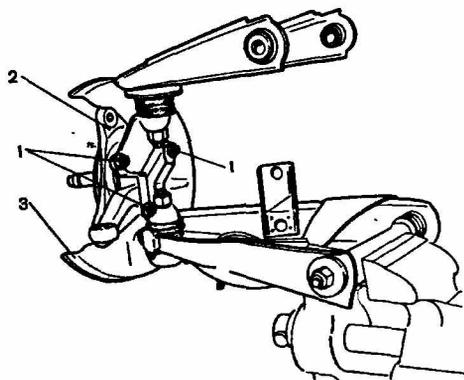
Узел подвески левого колеса, закрепенный на верстаке для разборки: 1 - гайки крепления рычага поворотного кулака, кронштейна крепления суппорта и защитного кожуха к поворотному кулаку; 2 - кронштейн крепления суппорта; 3 - защитный кожух тормозного диска
